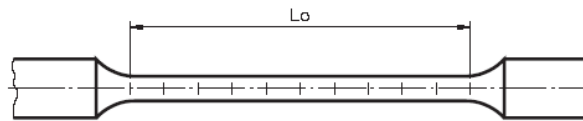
Corpo de prova para ensaio de tração antes do ensaio.
